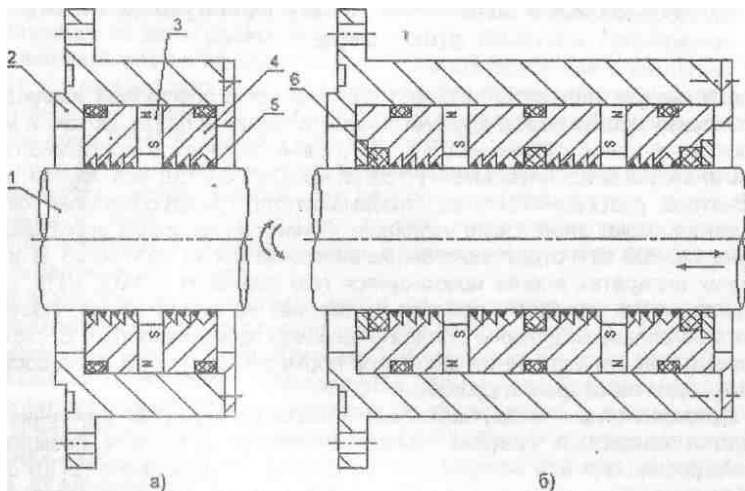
а – классический МЖГ; б – традиционный МЖГ: 1 – вал; 2 – корпус из немагнитного материала; 3 – постоянный магнит; 4 – полюсная приставка; 5 – магнитожидкостный уплотнитель; 6 – резиновое кольцо
